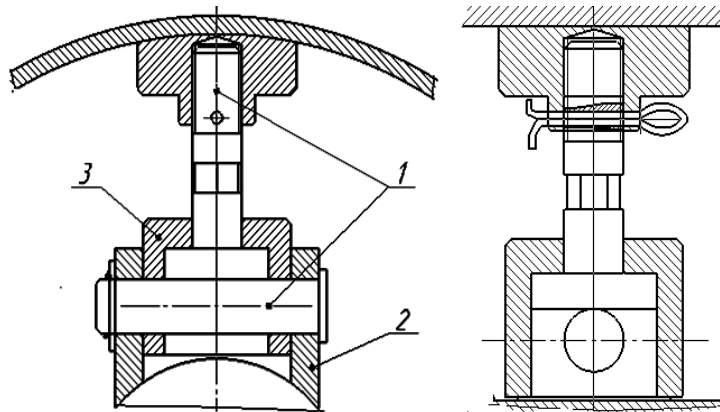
Передняя опора: 1 – пальцы; 2 – проушины крепления; 3 – втулка
